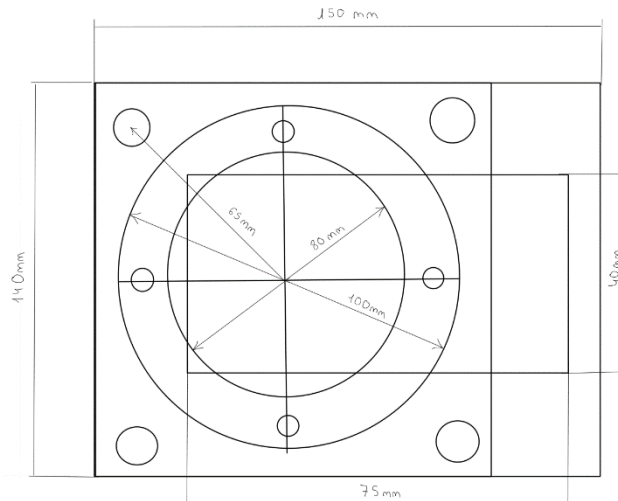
Vista en planta de las dimensiones de las placas de soporte del actuador lineal
